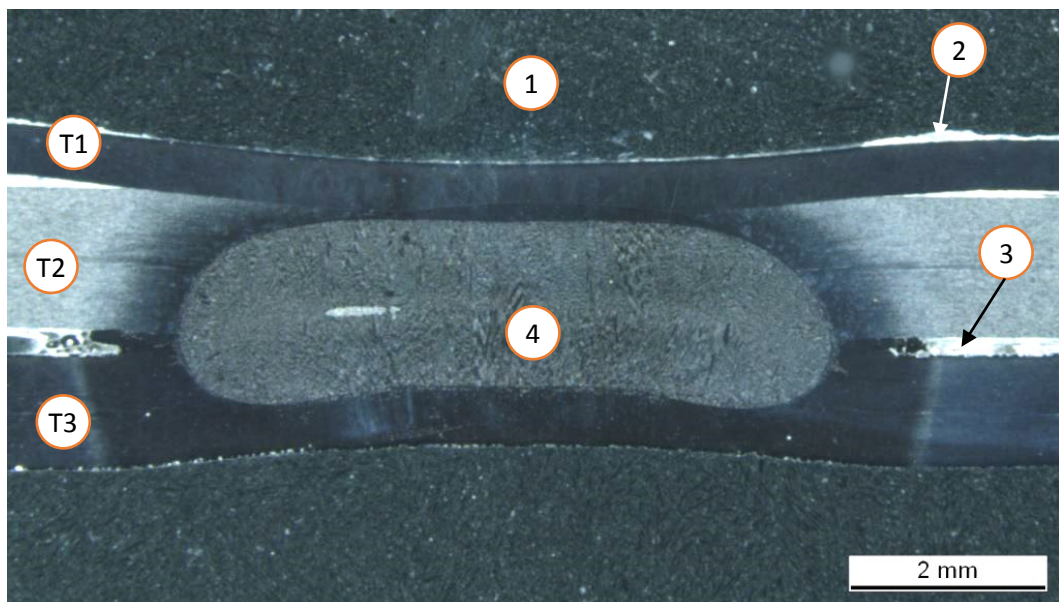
Coupe macrographique d'un point soudé (9 kA – 470 ms – 4 kN).
